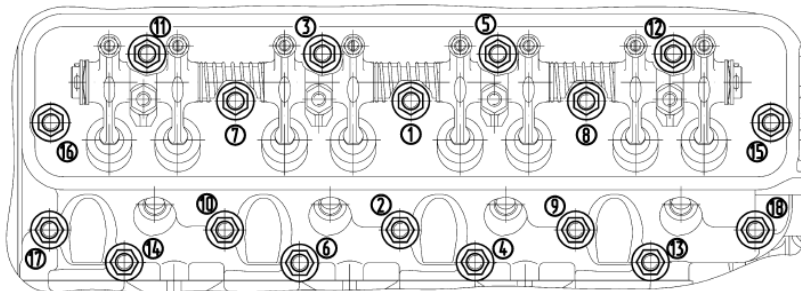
Порядок підтяжки гайок кріплення головки циліндрів
